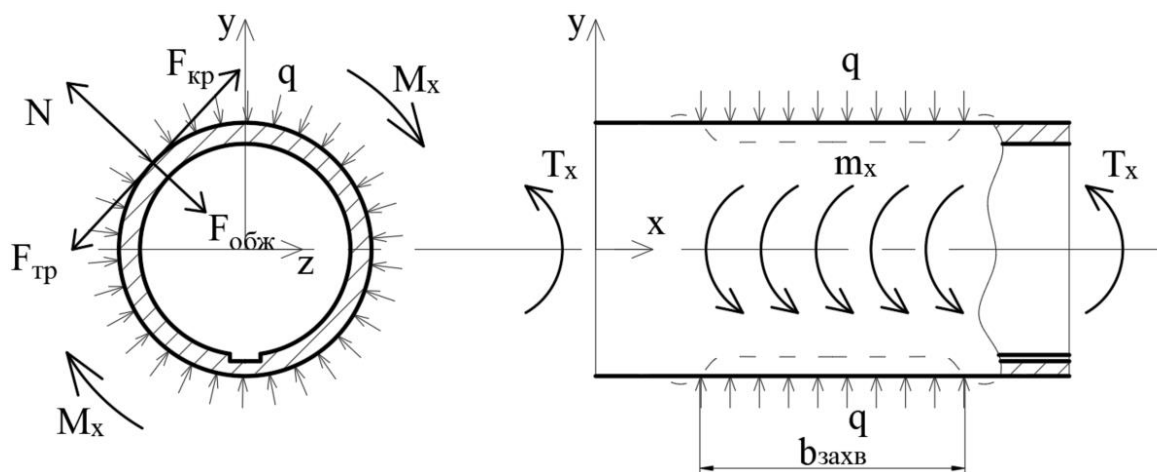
Расчетная схема приложения крутящего момента к трубопроводу. Нагрузки, граничные условия
